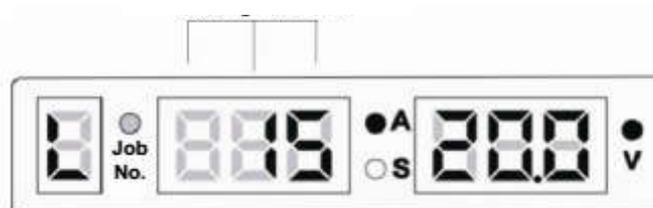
Пользовательский интерфейс для блокировки диапазона регулировки сварочного тока
